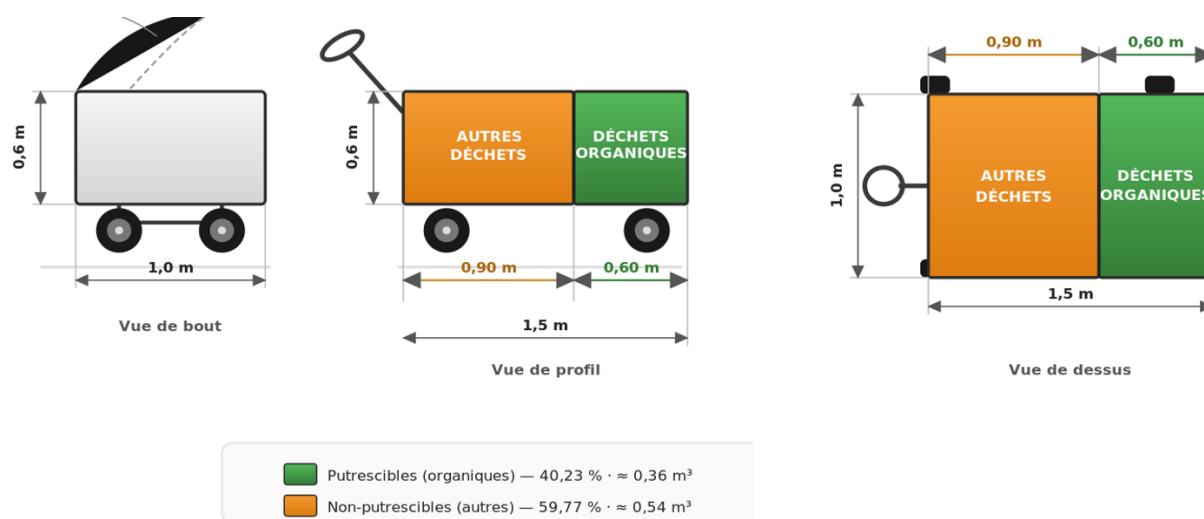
Dimensions du véhicule KALESA - Vues arrière, latérale et de dessus
